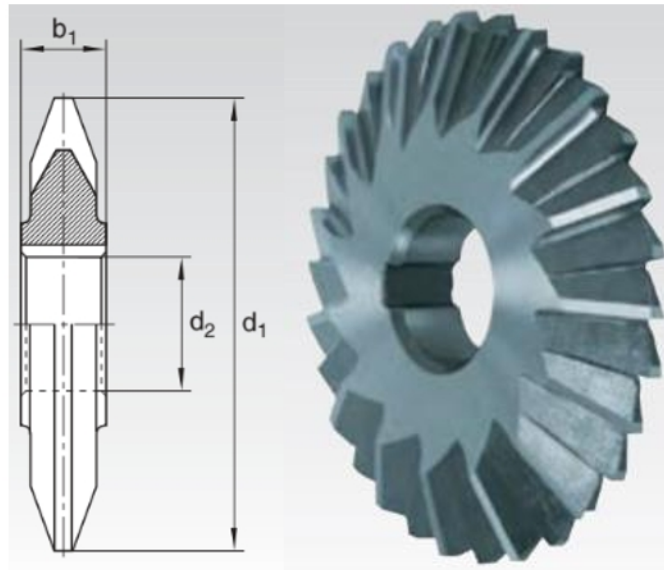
Дискава фреза 2500 [3, с. 88]
